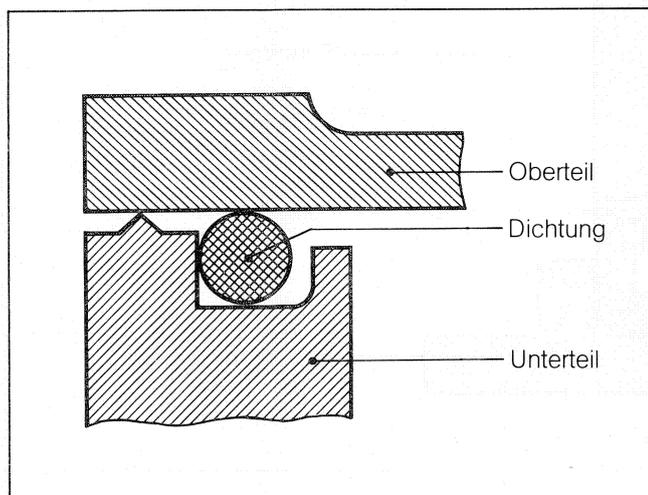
Ultraschallschweißen von Formteilen mit eingelegter Dichtung
